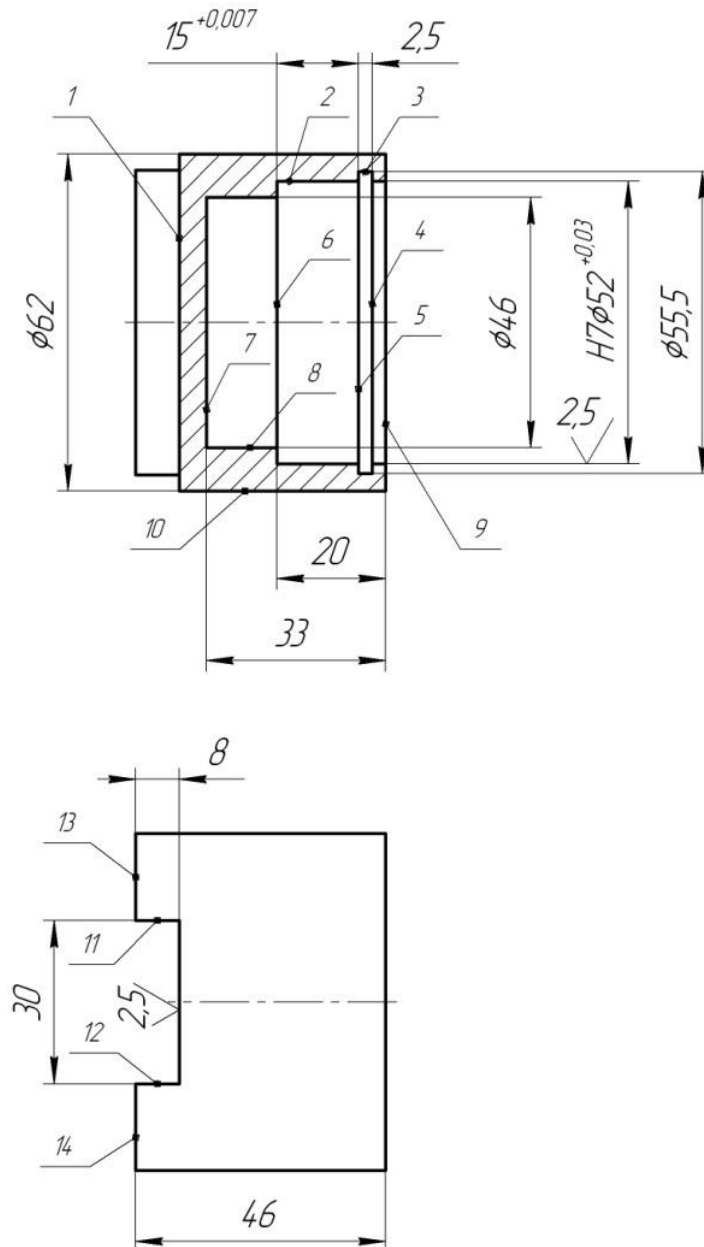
Креслення деталі «втулка опорна» та її основні поверхні
